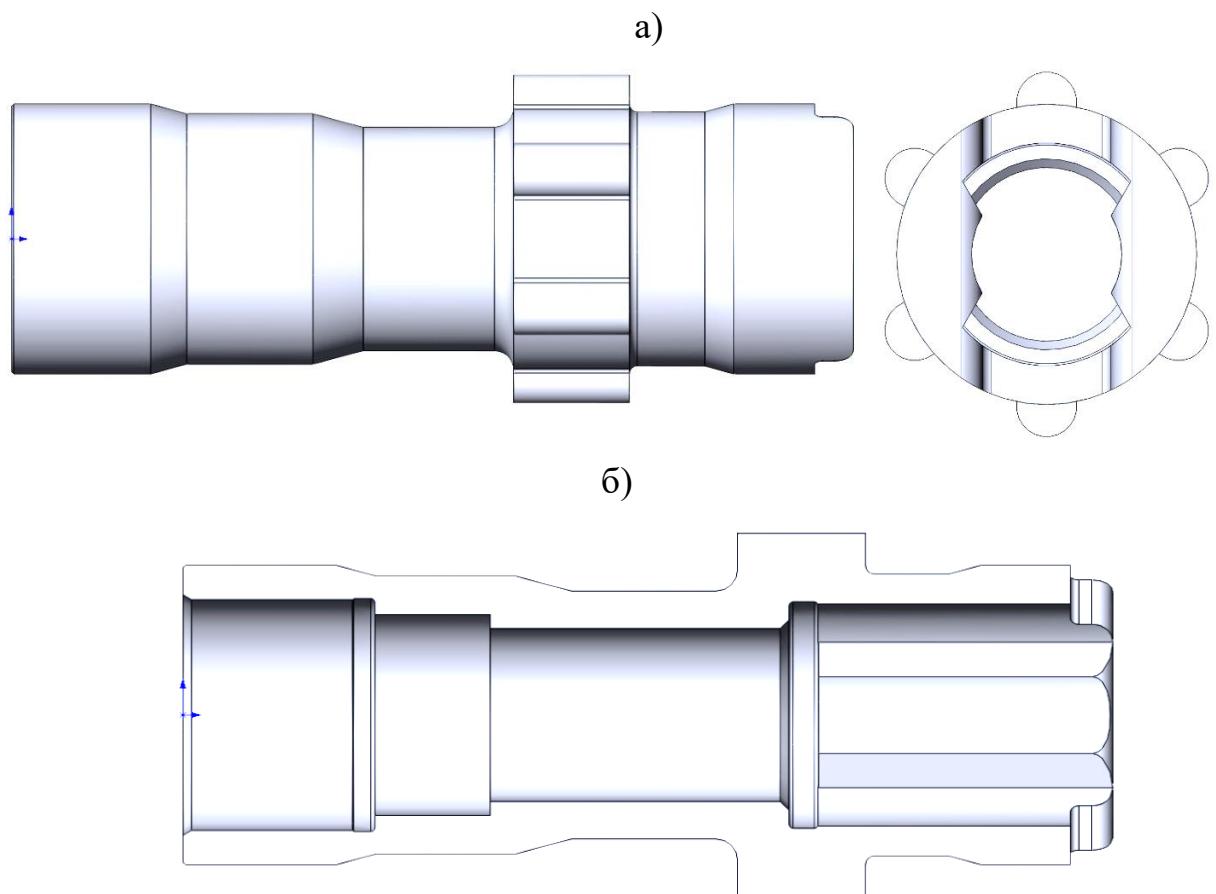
конструкція шпинделя: а – загальний вид шпинделя, б – переріз шпинделя
